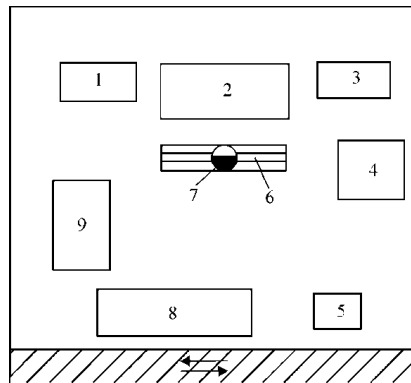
Робоче місце газозварювальника (площа 21,2 м²): 1 – столик приймальний; 2 – стіл для газозварювальних робіт; 3 – генератор ацетиленовий; 4 – тумбочка для інструменту; 5 – ящик для піску; 6 – підставка-решітка; 7 – стілець; 8 – стелаж для деталей; 9 – стійка для балонів з киснем і ацетиленом (візок).
